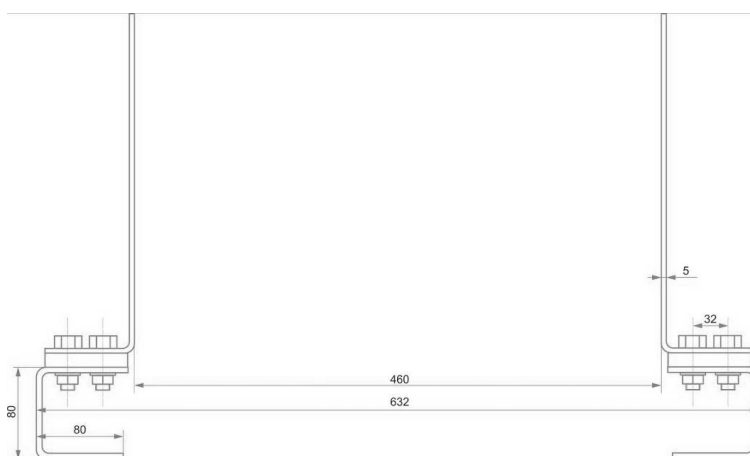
Загальний вид кріплення задніх опір двигуна до рами АТЗ (вид попереду)
